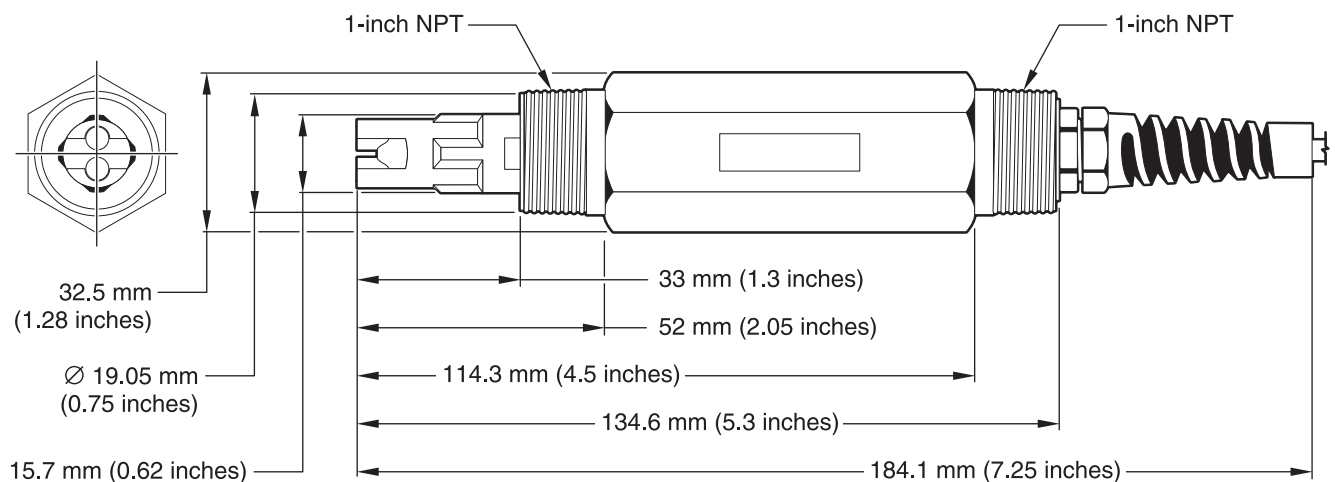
Drukdichte sensor (met gegoten aansluitingskast)
